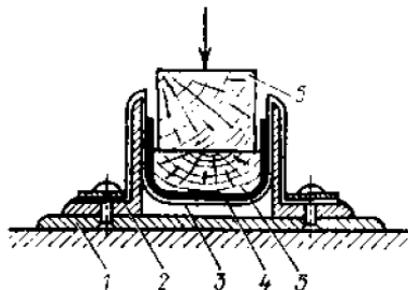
Схема приспособления с гибкой лентой для облицовывания криволинейных поверхностей брусков в гидравлических прессах с обогреваемыми плитами
